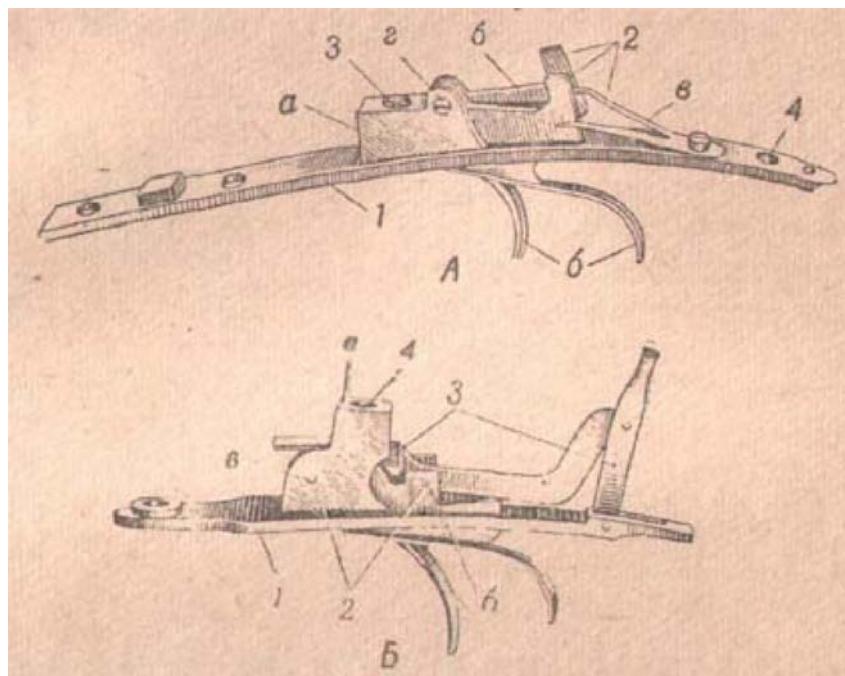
Нижняя личина со спусковым механизмом типичной конструкции для двуствольных ружей с горизонтально спаренными стволами: А - ружей моделей ИЖБ-36 и ИЖБ-46: 1 - нижняя личина; а - упор (прилив); 2 - спусковой механизм; б - спусковые крючки (гашетки); в - пружина спусковых крючков; г - ось спусковых крючков; 3 - гнездо для винта упора; 4 - отверстие для хвостового винта; Б - ружьё с системой ударного механизма, смонтированного в коробке: 1 - нижняя личина; а - прилив (упор); 2 - спусковой механизм; б - спусковые крючки (гашетки); в - ось спусковых крючков; 3 - предохранитель; 4 - гнездо винта упора
